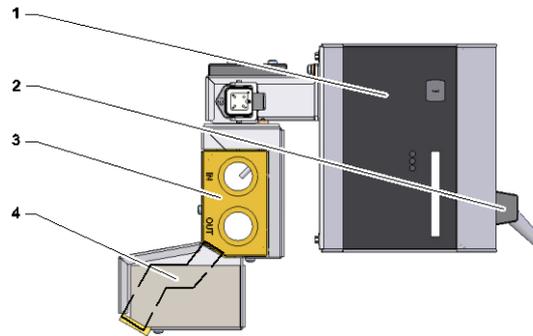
Общий вид конструкции: отдельно стоящий прибор
